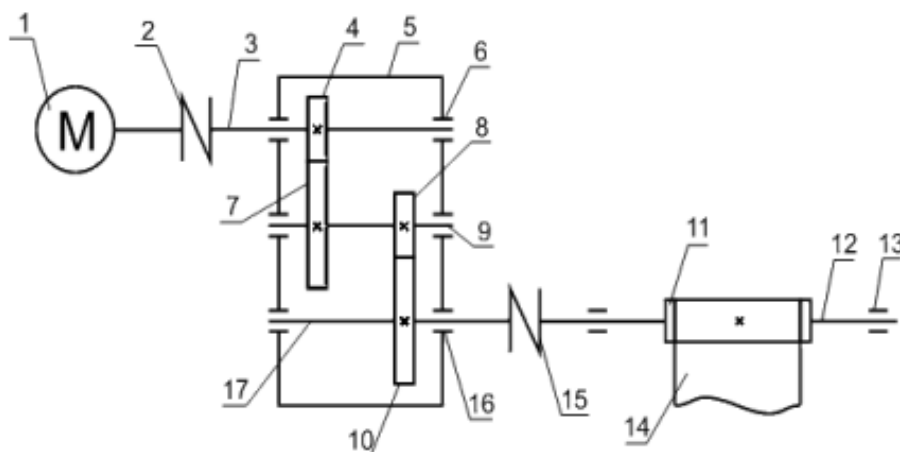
Кинематическая схема ленточного конвейера (1 – электродвигатель; 2,15 – муфты (МУВП, цепная); 3 – быстроходный (ведущий) вал; 4,7 – 1-ая зубчатая ступень; 5 – корпус; 6,9,16 – подшипниковые узлы; 8,10 – 2-ая зубчатая ступень; 11 – приводной барабан; 12 – вал; 13 – подшипниковый узел; 14 – конвейерная лента; 17 – тихоходный (ведомый) вал)
